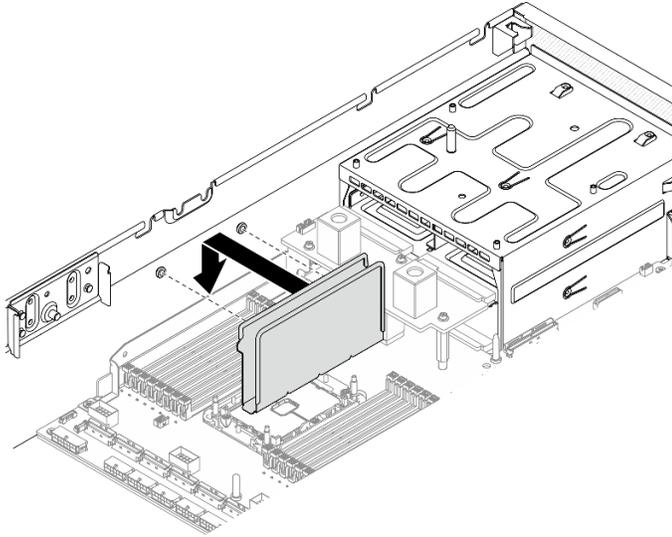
Anbringen der Kabelabdeckung am Gehäuse
